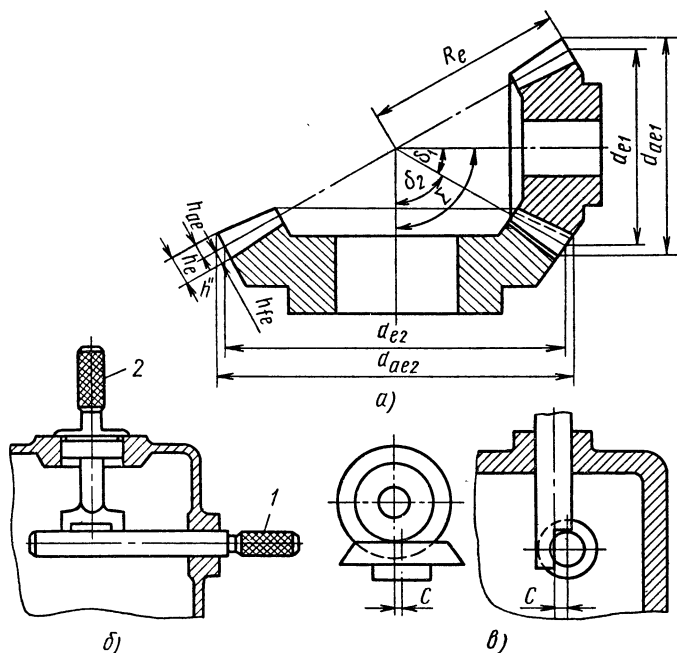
Схема конической зубчатой передачи (*a*), проверка перпендикулярности осей колес (*б*), проверка совмещения осей (*в*)
